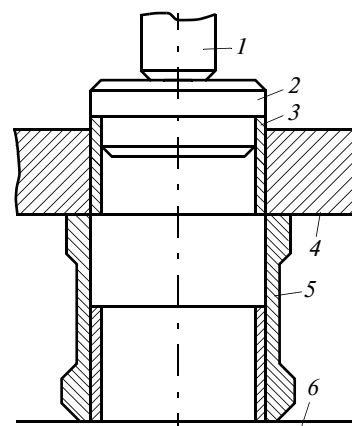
Схема для перемещения свёрнутой пластины из пресс-формы в деталь:
